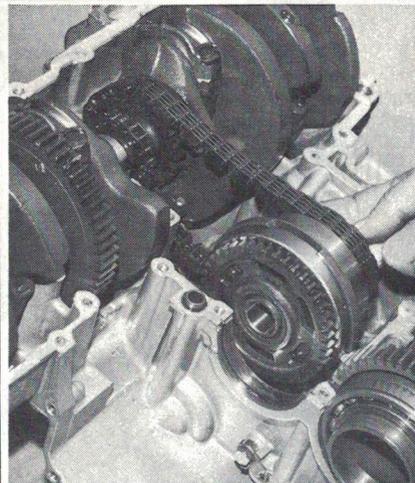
Roue libre de démarreur (Photo RMT)
